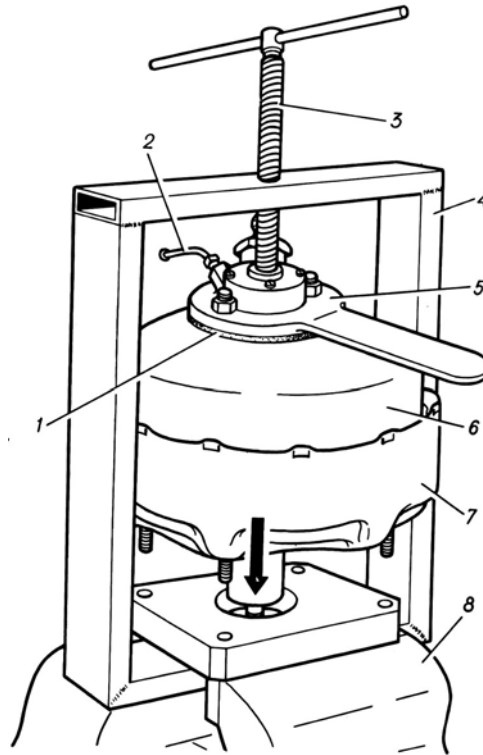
Приспособление для разборки и сборки усилителя: 1 - прокладка; 2 - трубка; 3 - винт; 4 - приспособление; 5 - заглушка; 6 - крышка; 7 - корпус; 8 - тиски
